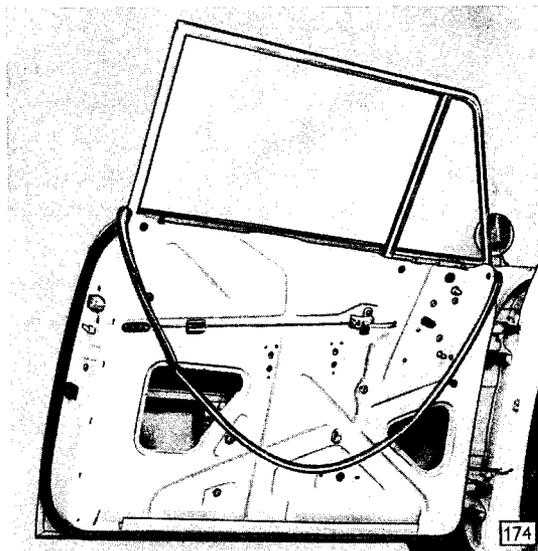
Türdichtung vom Fensterrahmen gelöst
